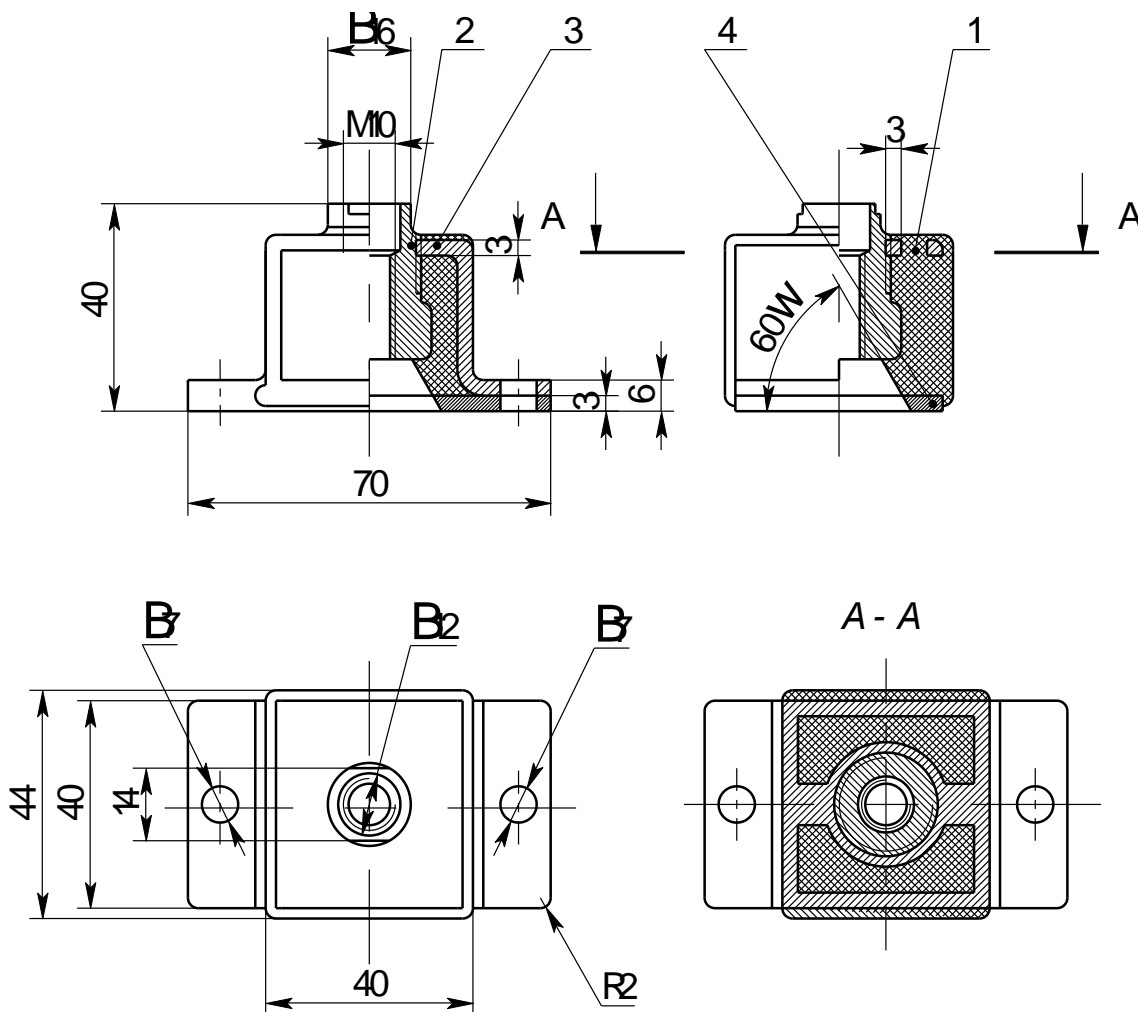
Двухмерная модель изделия: 1 – корпус; 2 – втулка; 3 – скоба; 4 – пластина.
